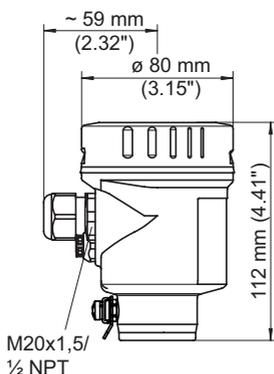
Корпуса в исполнении IP66/IP68 (0,2 bar), (с установленным модулем индикации и настройки корпус выше на 9 мм/0.35 in)
